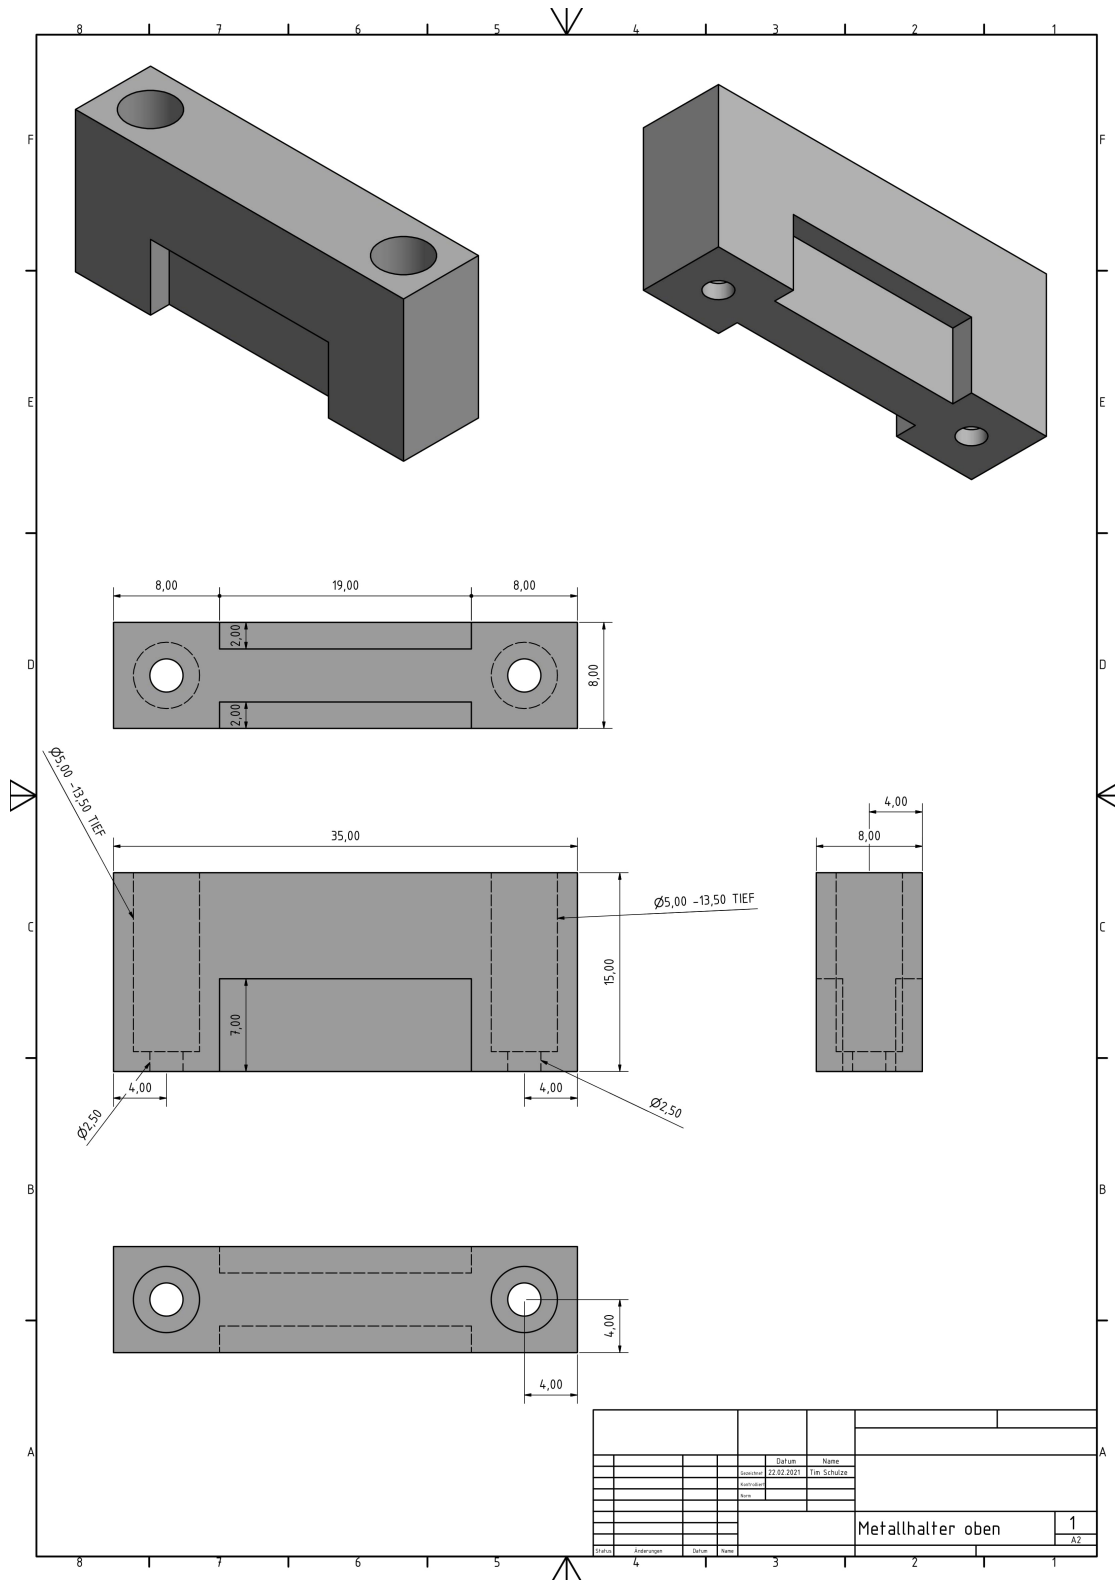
Technische Zeichnung des oberen gefrästen Metallhalters für die statischen und aktiverbaren Wellenleiter
